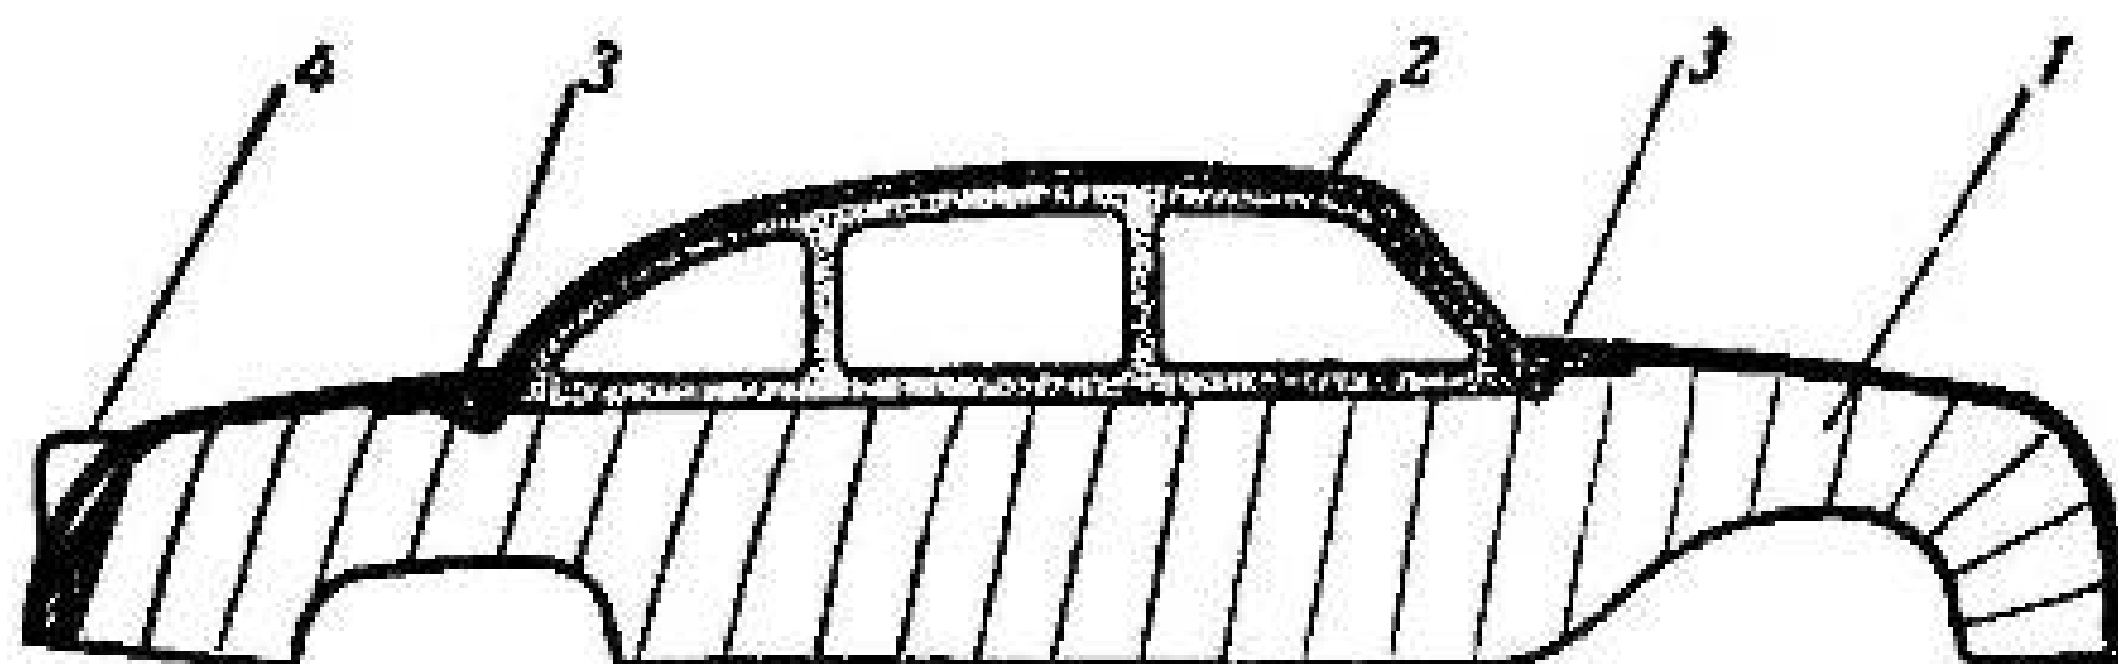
Разрез кузова модели, изготовленного комбинированным способом:
